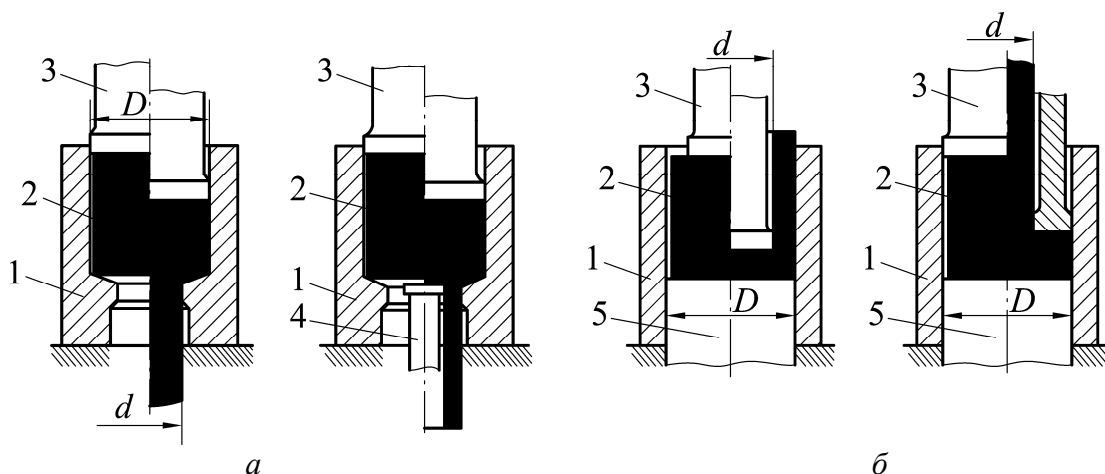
Схема прямого (а) и обратного (б) выдавливания: 1 – матрица; 2 – заготовка; 3, 4 – пуансоны; 5 – выталкиватели
